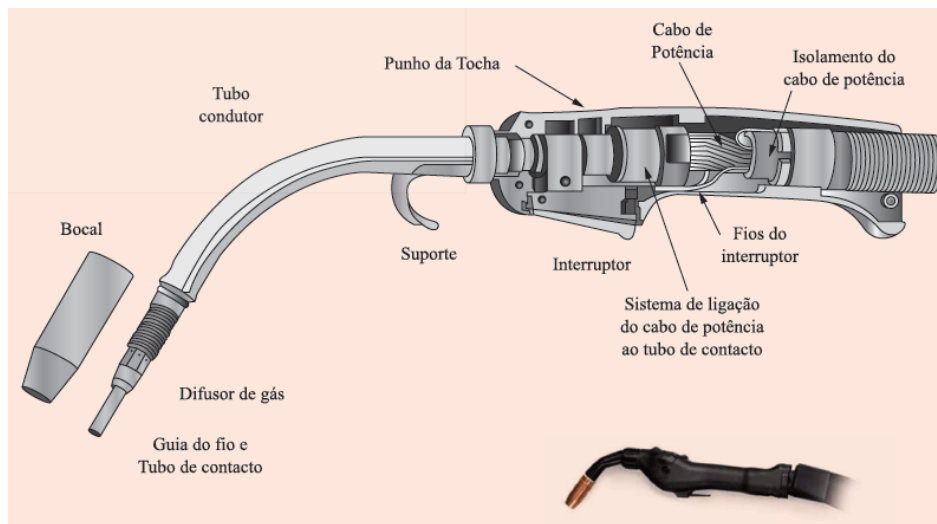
Representação esquemática de uma tocha para soldadura MAG (Retirado de: Silva, 2016)
